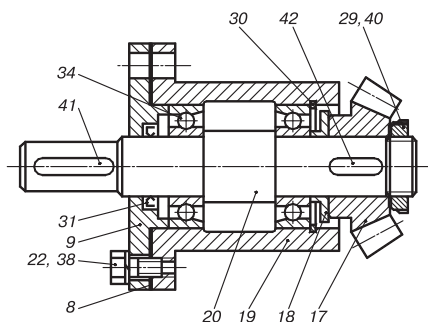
Вал быстроходный в конструктивном исполнении редуктора (см. рис. 5.3)
